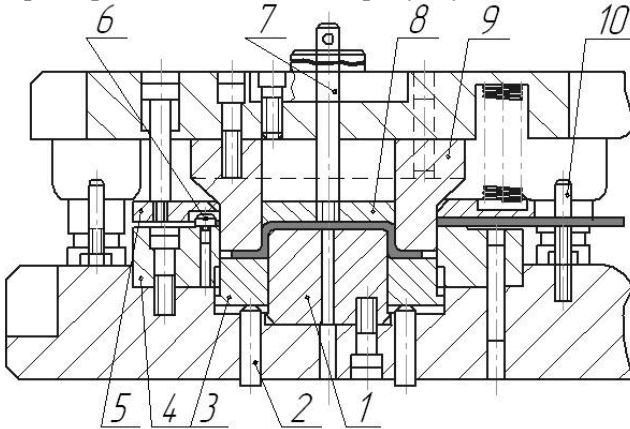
Штамп сумісної дії для вирубкки і витяжки
